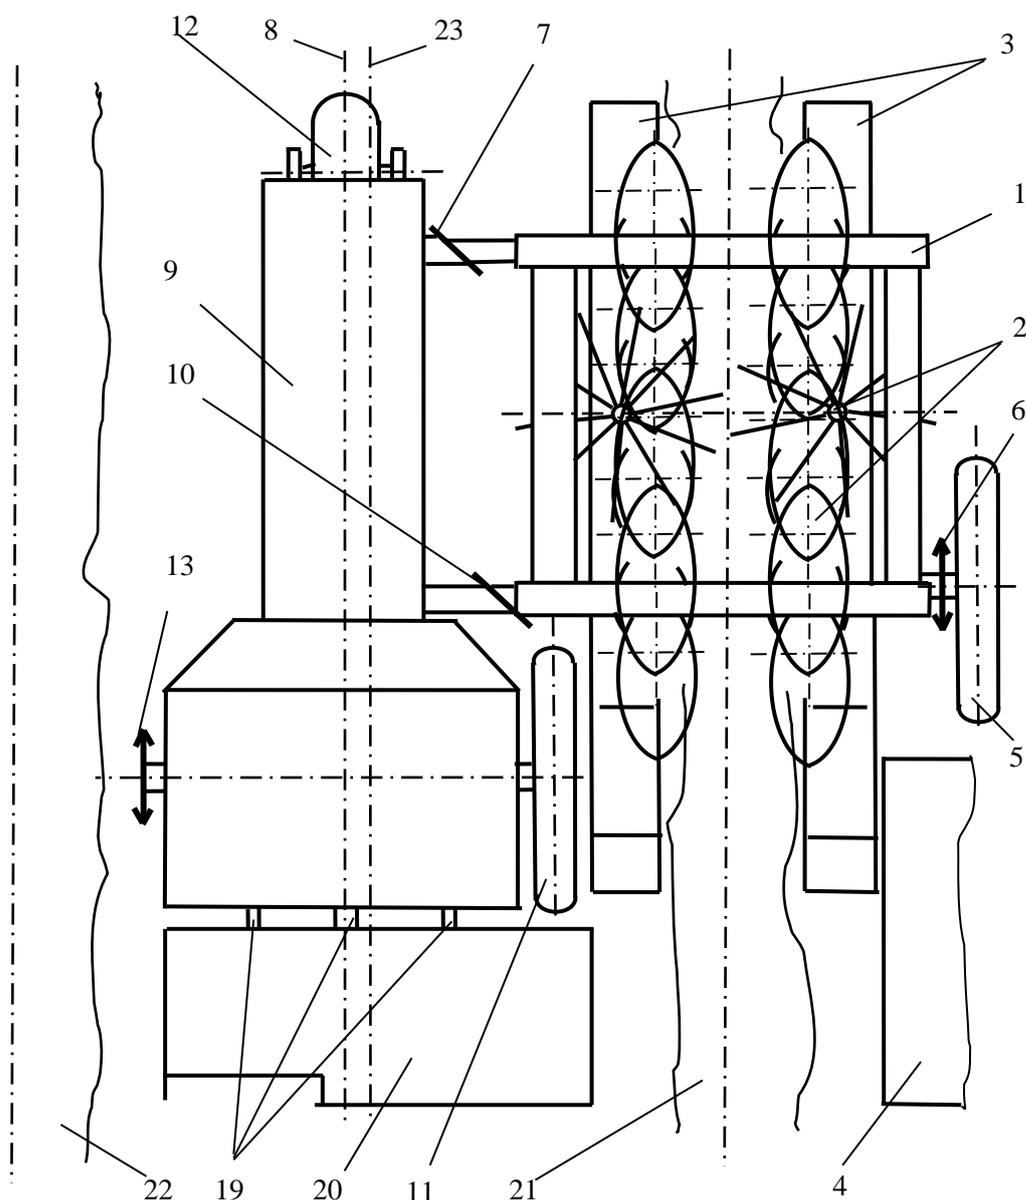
Компонировочное решение ягодоуборочного комбайна (вид сверху)
